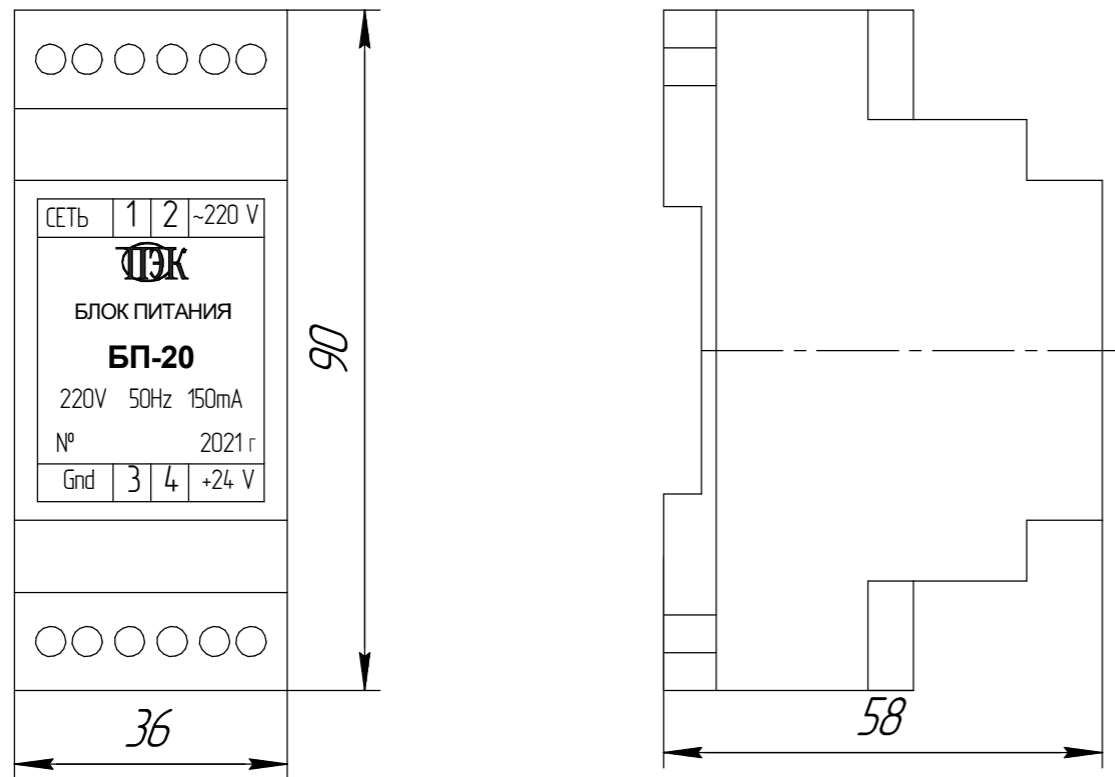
Габаритные размеры блока БП-20 (на DIN-рейке)
